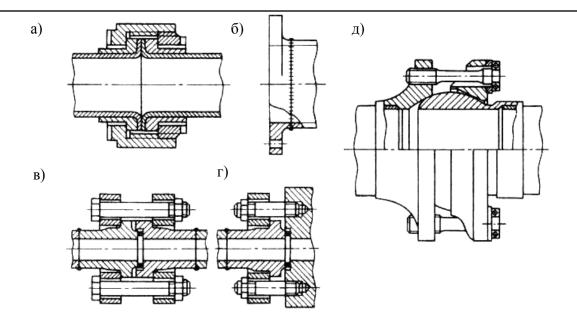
Схемы разъемных неподвижных беспрокладочных фланцевых соединений с развальцовкой труб на торен (а), сварных соединений (б), с накидным фланцем (в, г) и сферического соединения (б)
